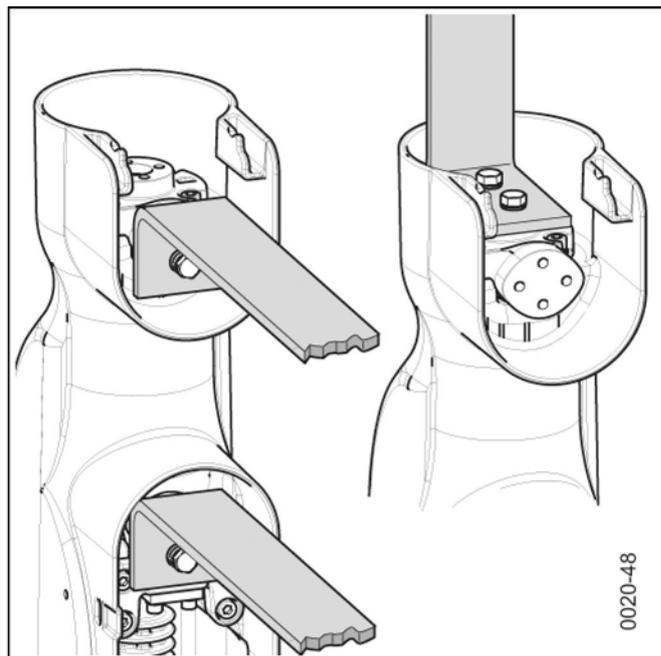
Вертикальная установка шин (угловых). Пример для номинального тока 1250 А
